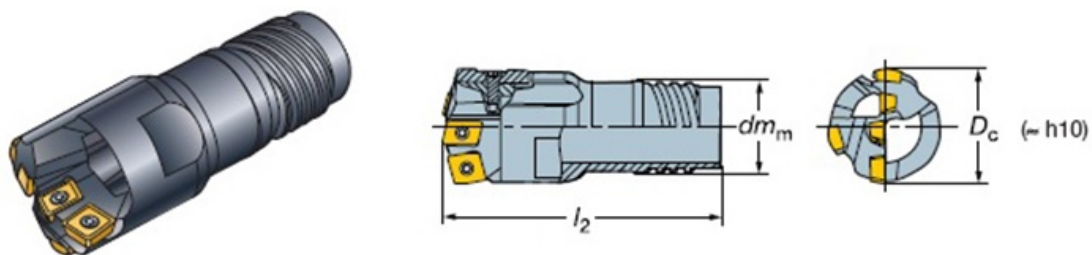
Конструкция головки для глубокого сверления CoroDrill 800.20
